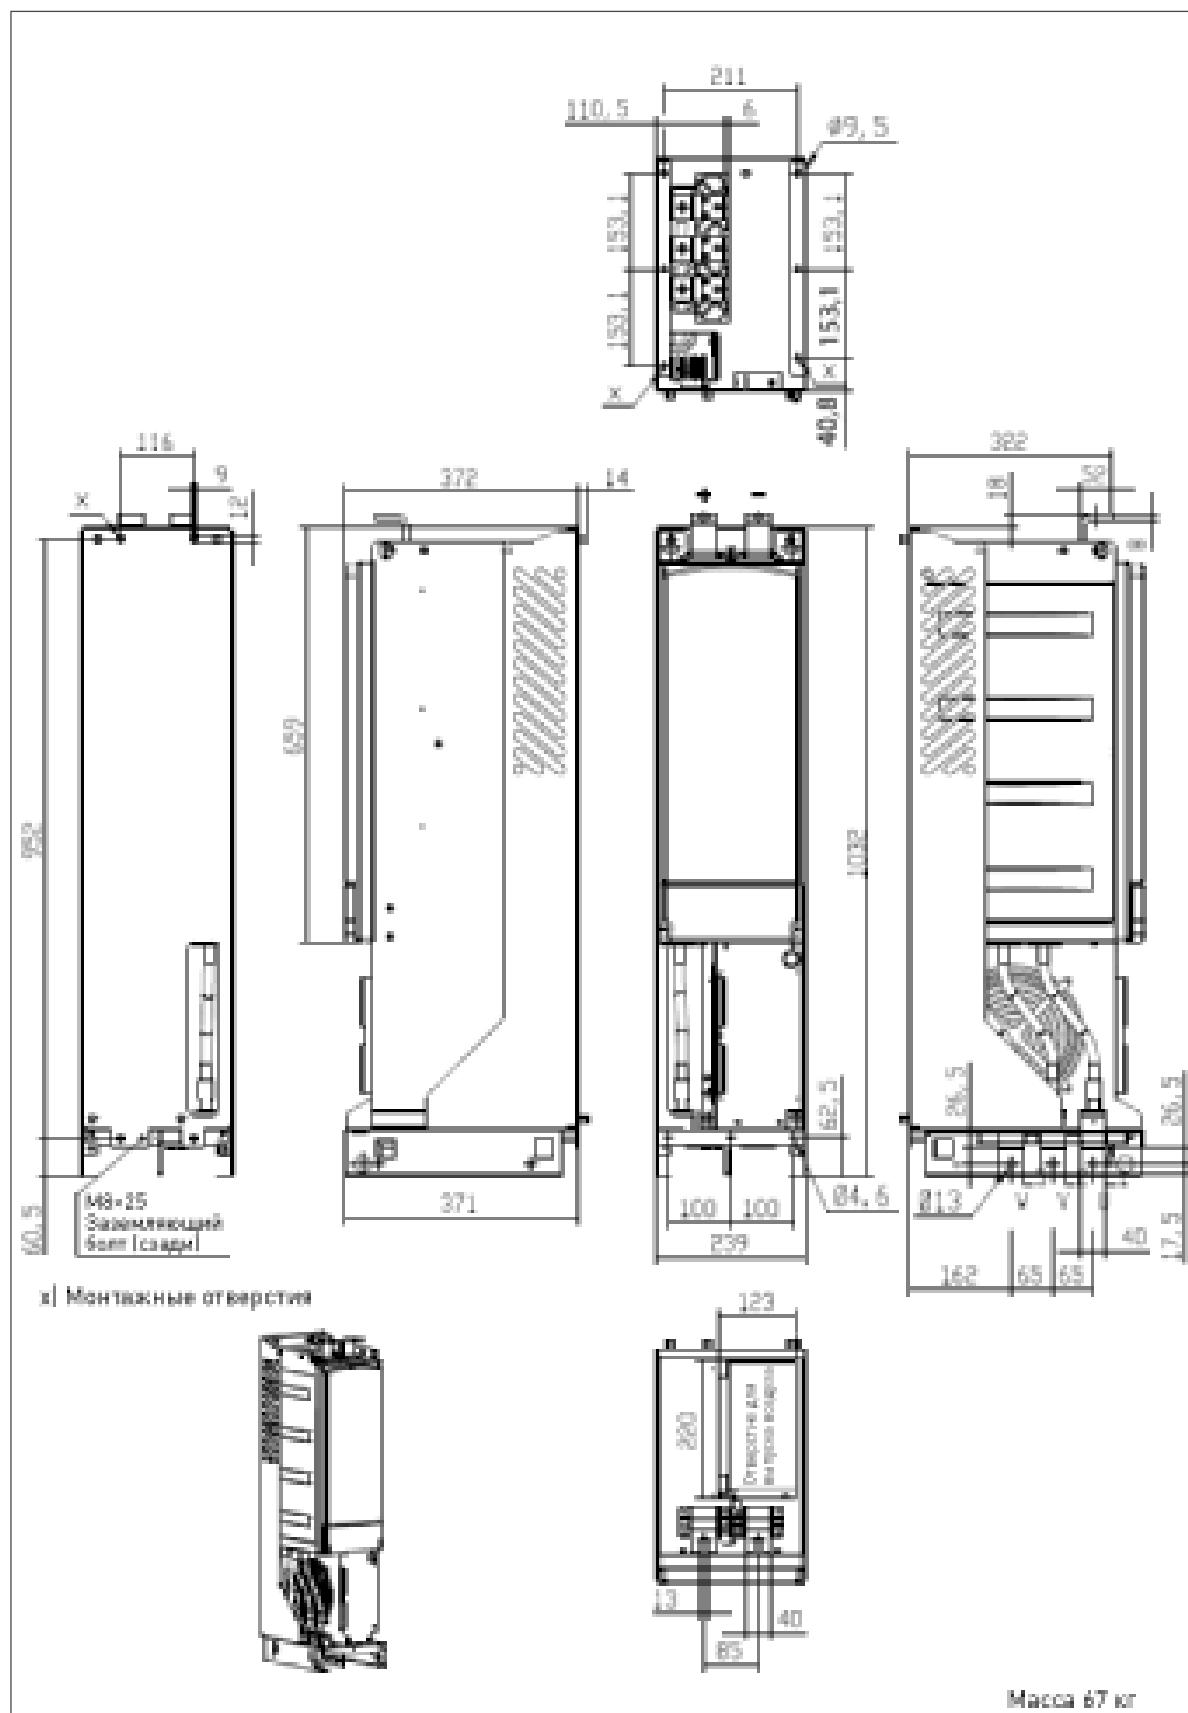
Габариты инвертора VACON® NXI, типоразмер F19
